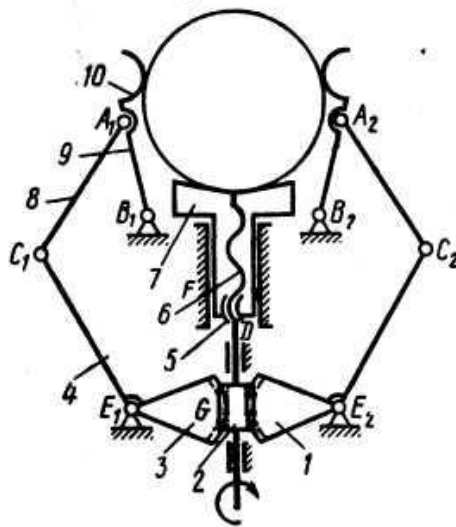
Конструктивна схема важільного ЗП з регульованими самоцентрувальними захватами
